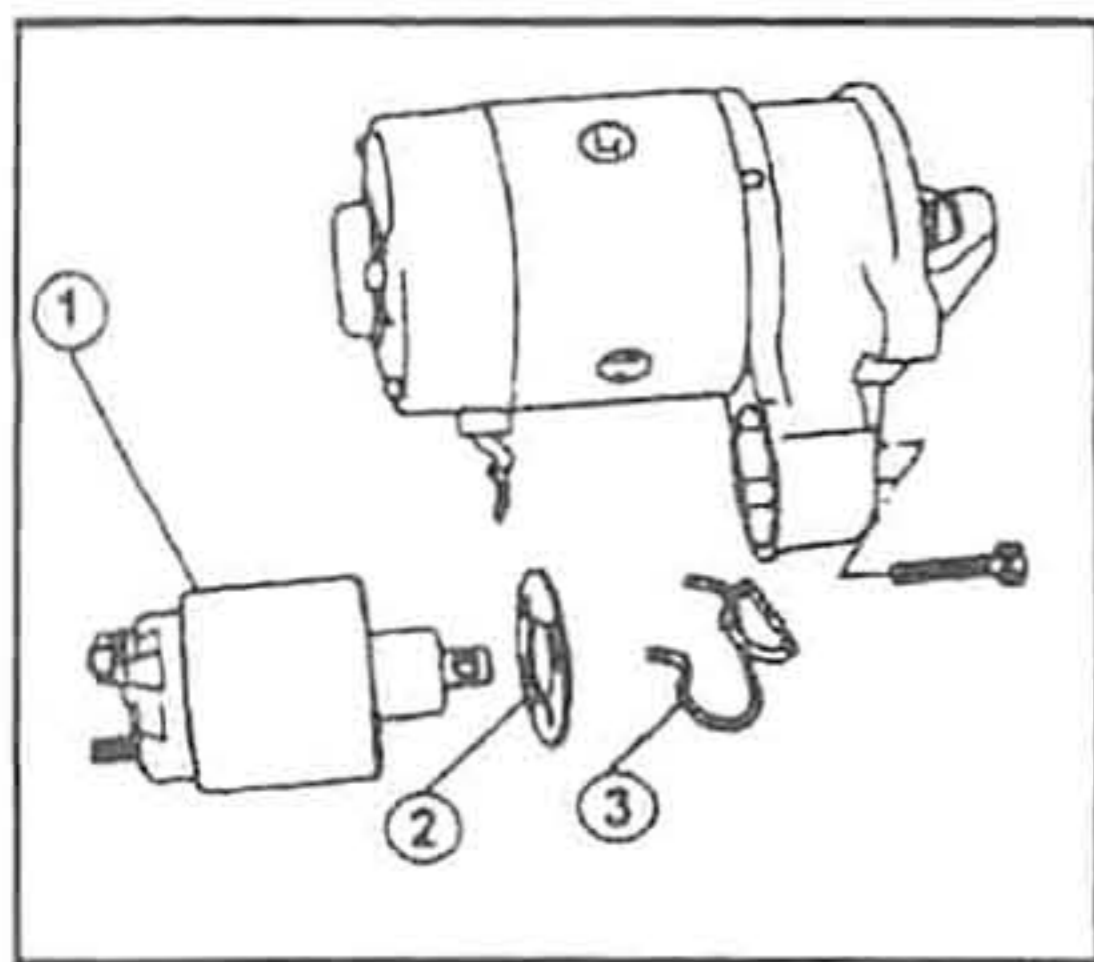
1. Магнитный выключатель. 2. Пылезащитная крышка. 3. Пружина.
